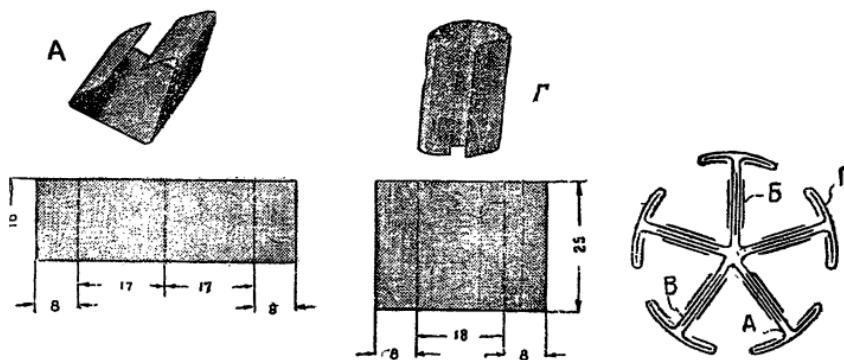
Основные детали и конструкция пятиполюсного якоря.
